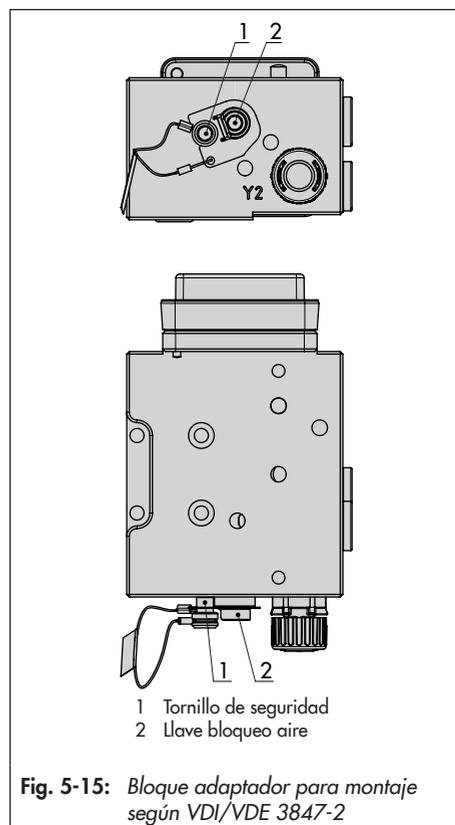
Bloque adaptador para montaje según VDI/VDE 3847-2
